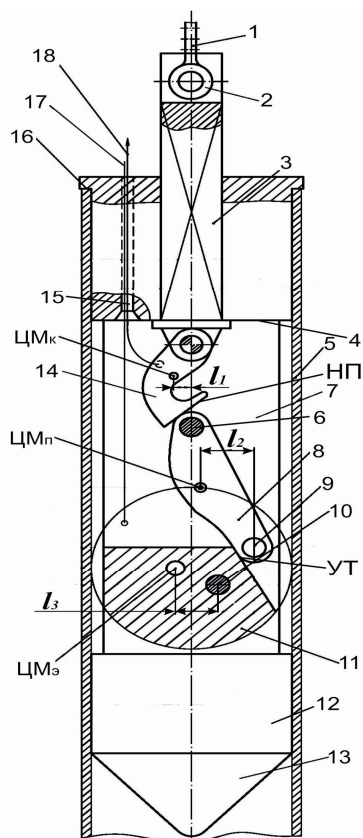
Полуавтоматический эксцентриковый захват трубы: 1 – канат, 2 – ось устройства подвеса, 3 – ползун прямоугольного сечения, 4 – упорный торец ходового цилиндра, 5 – труба, 6 – ось проушины верхняя, 7 – паз П для размещения к нему крюка, проушины и эксцентрика, 8 – проушина, 9 – ось проушины нижняя, 10 – ось эксцентрика, 11 – эксцентрик, 12 – корпус ходового цилиндра, 13 – конус направляющий, 14 – крюк, 15 – отверстие для прохода канатов, 16 – посадочный торец, 17 – канат поворота эксцентрика, 18 – канат поворота крюка, ЦМ_к – центр масс крюка, ЦМ_п – центр масс проушины, ЦМ_э – центр масс эксцентрика, НП – направляющая поверхность, УТ – упорный торец для проушины
